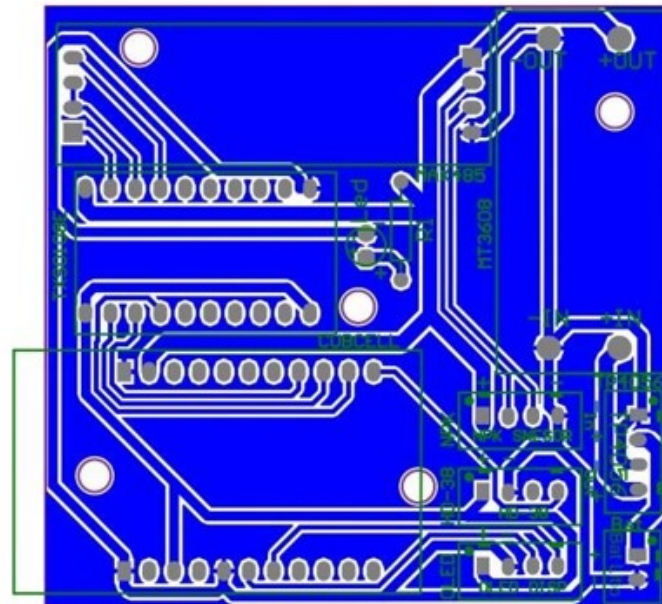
Placa en vista 2D (Diseño Reutilizado) [58].
